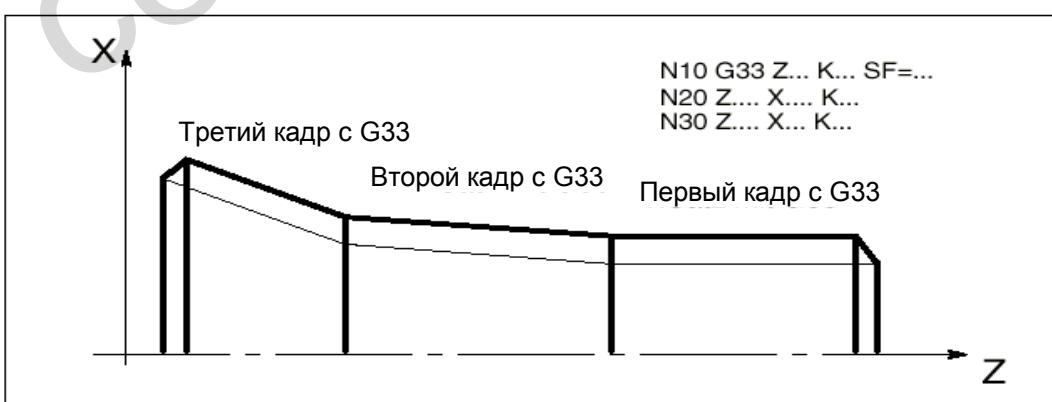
Пример многокадровой резьбы (соединение нескольких видов резьбы)
